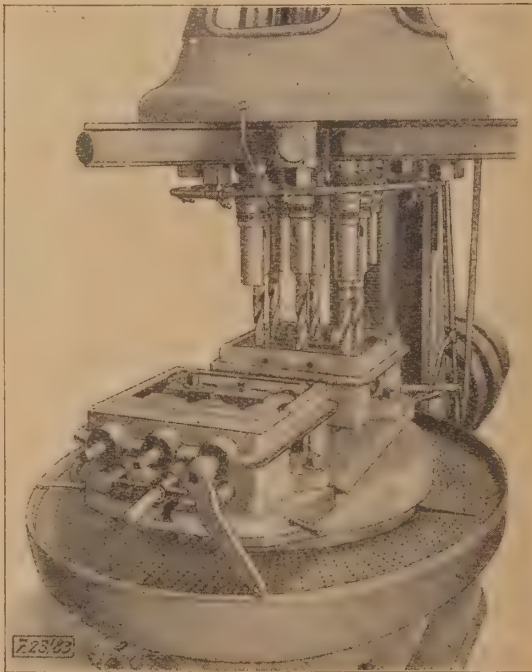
Mehrspindel-Bohrmaschine. Tisch mit drehbarer Platte.
